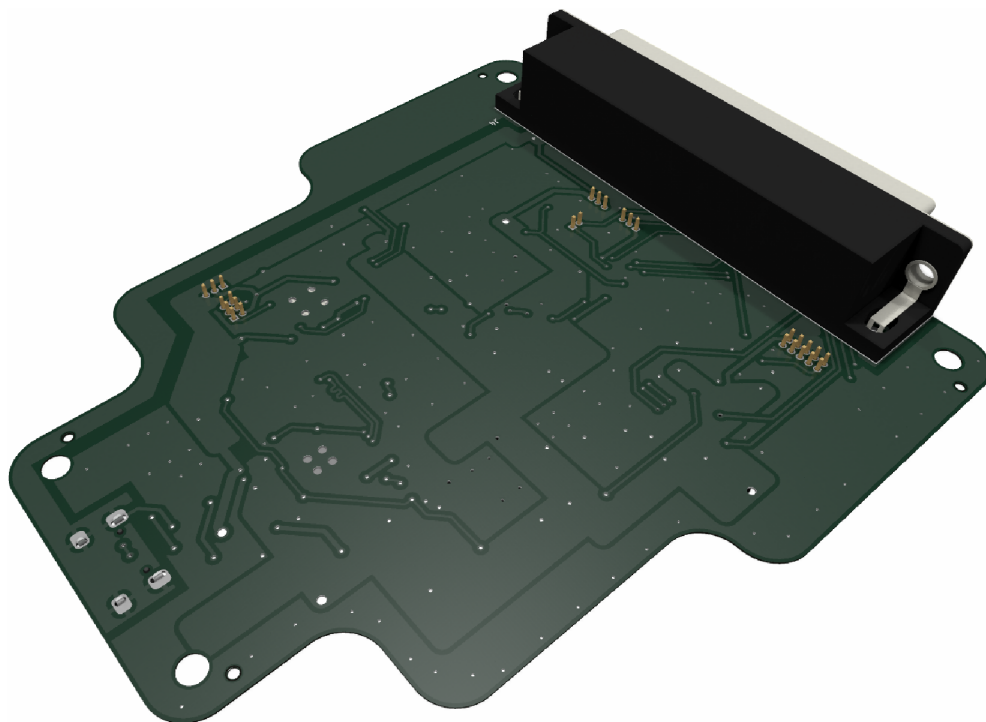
3D model testovací DPS – pohled shora po úhlem
